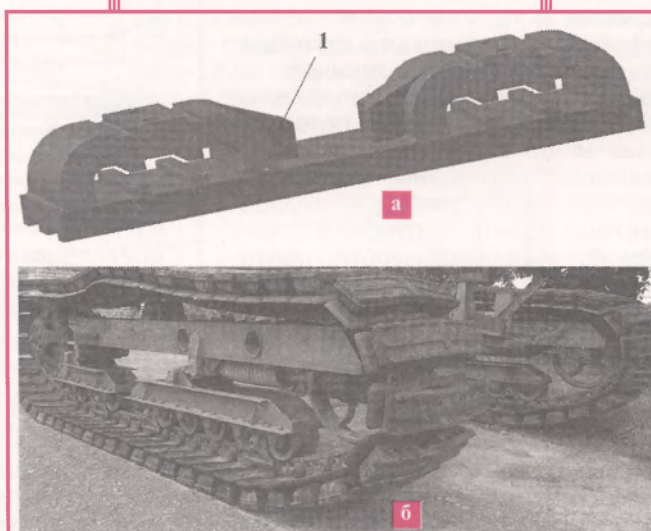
Резинокордный трак: а – 3D-модель конструкции трака; б – гусеничная тележка с резинокордными траками комбайна «Амур-680»: 1 – центральный упор
